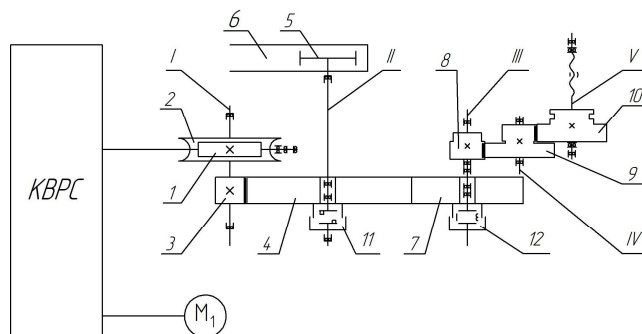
Кинематическая схема привода перемещения суппортов станка 1А667-FA:
